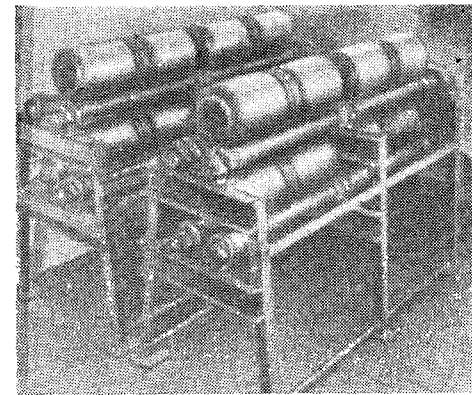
Размольный агрегат с барабанами из стали V2A для размола твердосплавных смесей (завод «Металльверк Планзее», Австрия)
